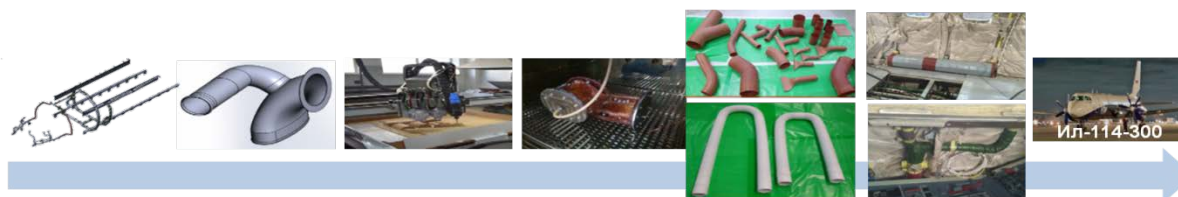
Производственный цикл изготовления заготовок жестких и гибких воздуховодов СКВ
